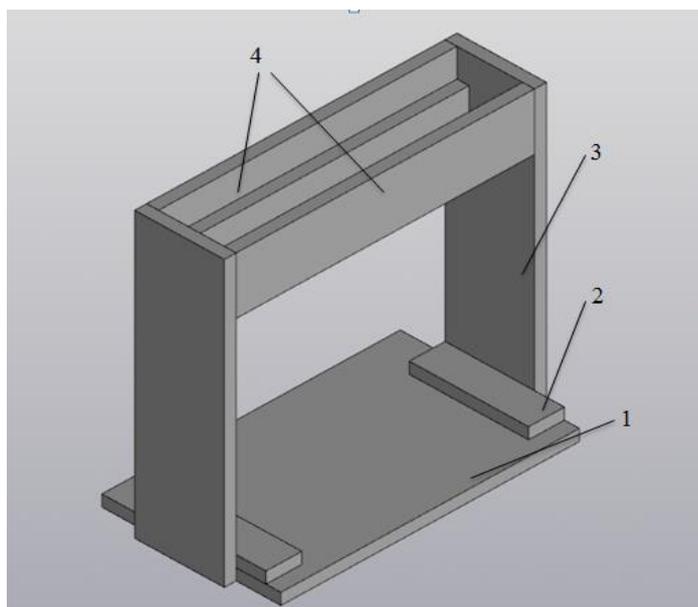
Модель корпуса (1-основание, 2-соединительный элемент, 3-стояк, 4-направляющие)
